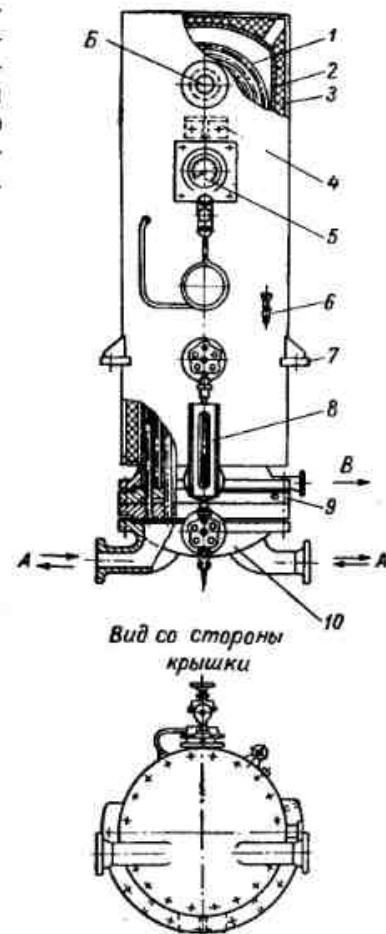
Подогреватель топлива типа ПН с U-образными трубками вертикального исполнения
